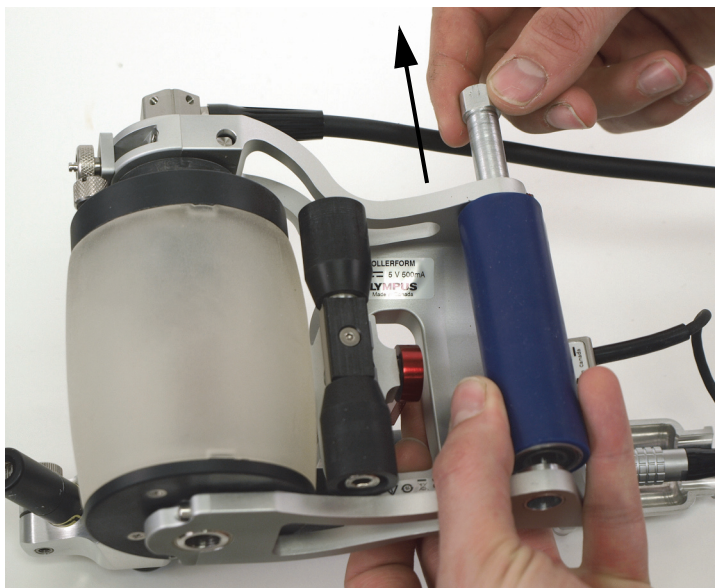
Dévissage de la vis de fixation du rouleau arrière
